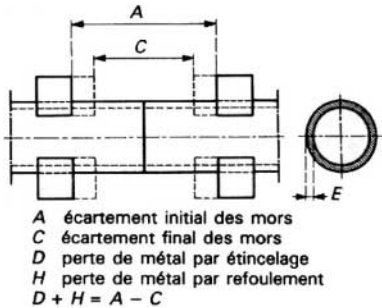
Soudage en bout : coupe d'une soudure
